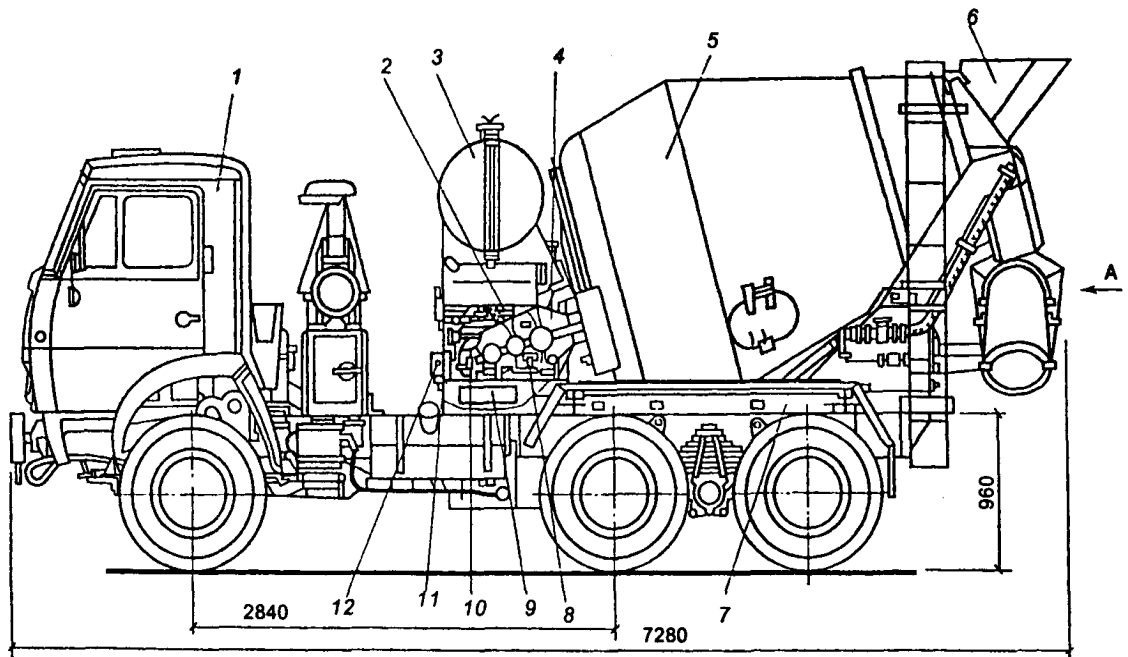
Автобетоносмеситель СБ-92-1А: 1 — насосы КамАЗ-5511; 2 — управление компрессором; 3 — бак для воды; 4 — привод смесительного барабана; 5 — смесительный барабан; 6 — загрузочно-разгрузочное устройство; 7 — рама; 8 — управление реверсом редуктора; 9 — панель контрольно-измерительных приборов; 10 — муфта сцепления; 11 — муфта насоса; 12 — управление подачей топлива
